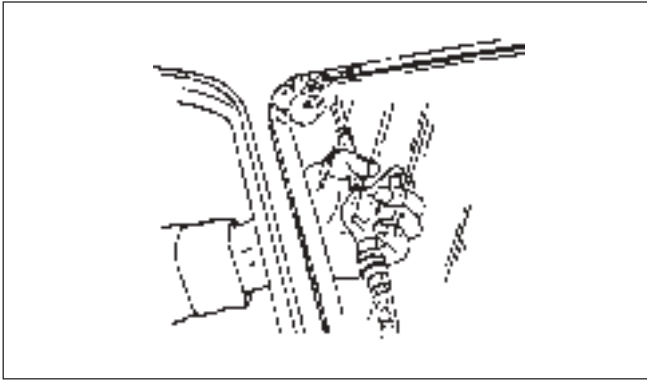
Testul cu aer și soluție spumantă asupra parbrizului
